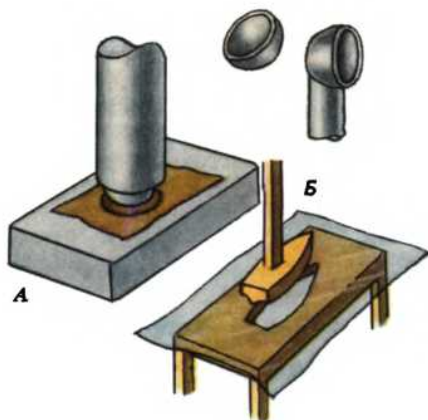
А — вытяжка металла давлением на свинце; Б — вытяжной штамп для пластмасс.
